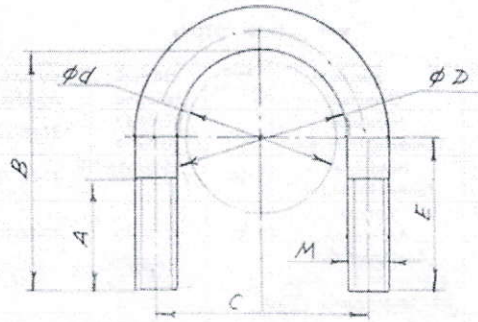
Конструкция и внешний вид скоб U-образных
